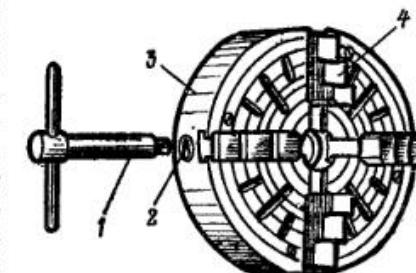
4-кулачковый несамоцентрирующий патрон
